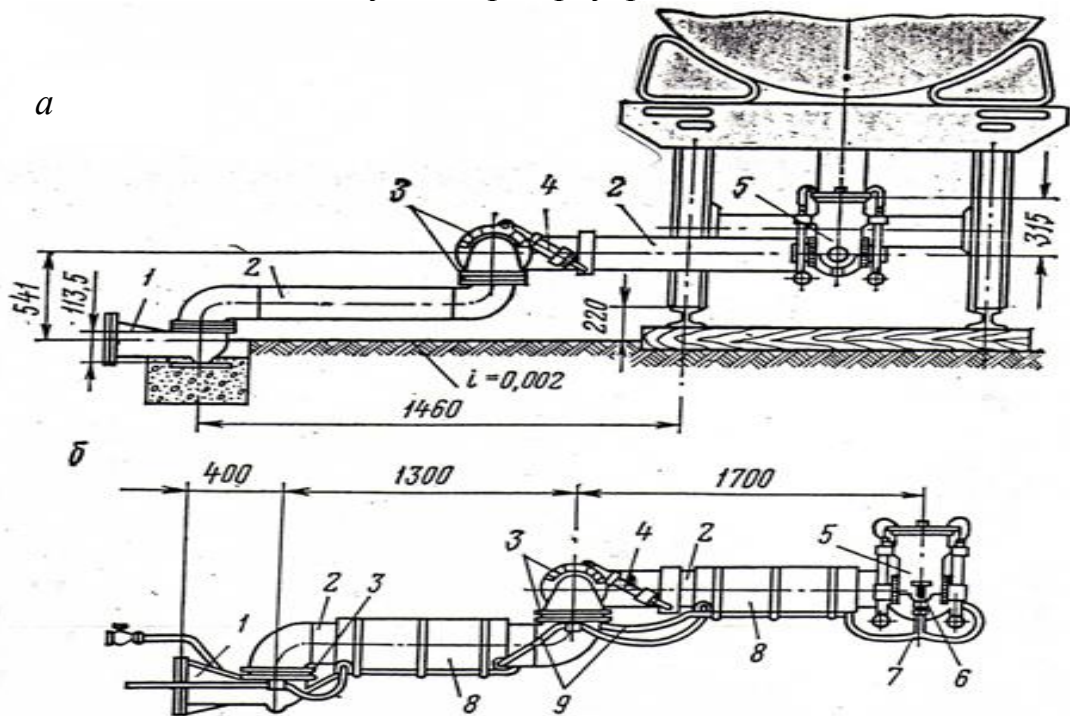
Установки для нижнего слива-налива светлых нефтепродуктов: а – АСН-7Б; б – АСН-8Б; 1 – коренной опорный патрубок; 2 – подвижной патрубок; 3 – шарнир; 4 – уравнивающее устройство; 5 – соединительная головка; 6 – кран; 7 – опорные шарниры; 8 – паровая рубашка; 9 – подводный шланг
